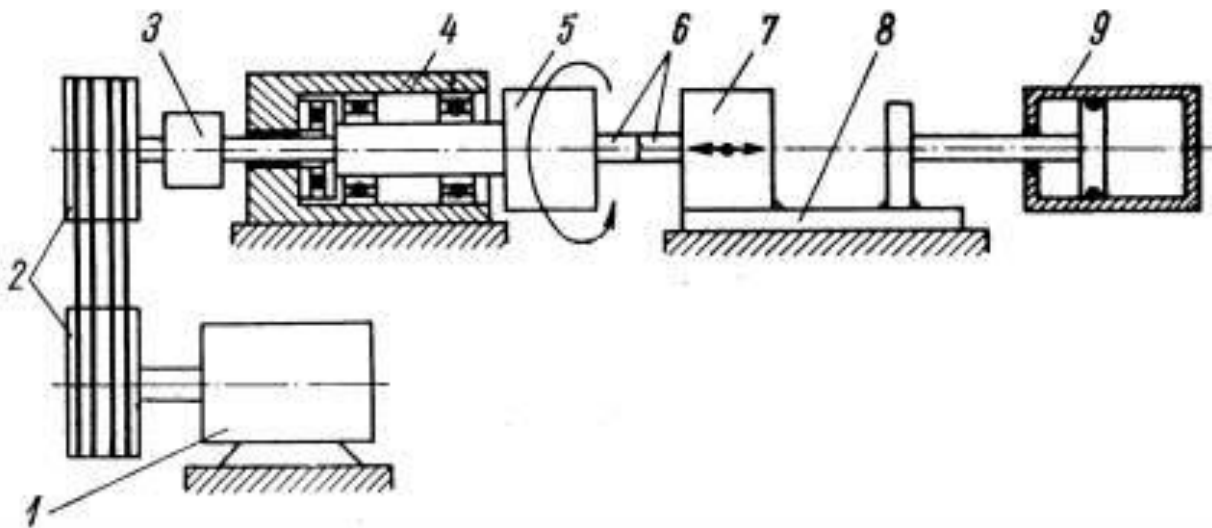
Принципиальная конструктивно-кинематическая схема машины для сварки трением.
